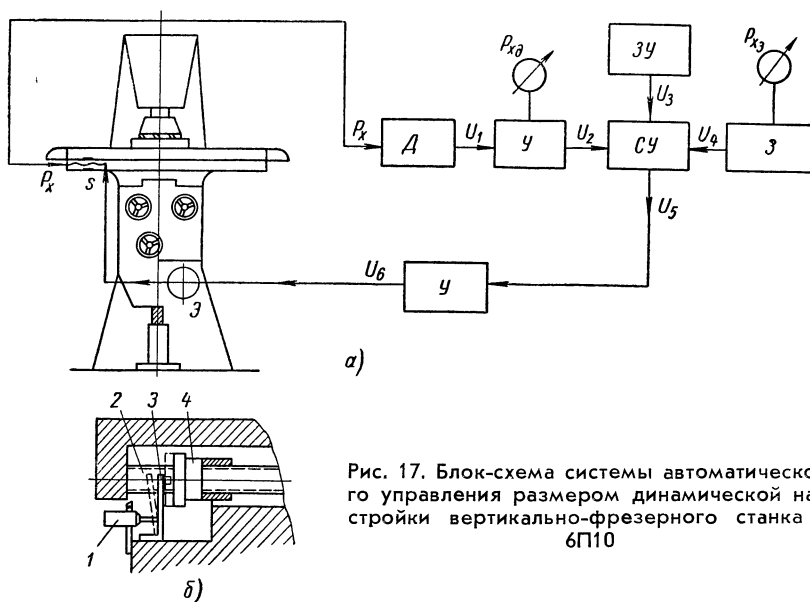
Блок-схема системы автоматического управления размером динамической настройки вертикально-фрезерного станка 6П10
